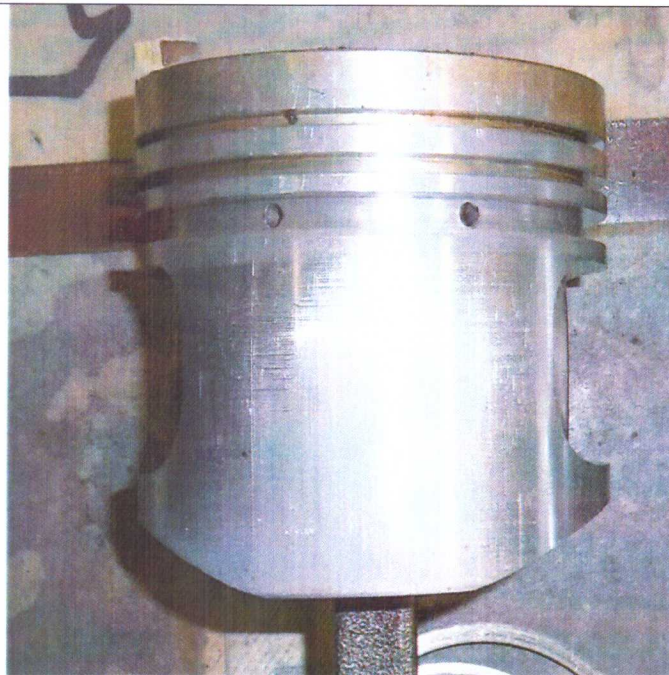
Внешний вид боковой поверхности поршня первого цилиндра по окончании длительных испытаний двигателя при работе на базовом масле Castrol EDGE с добавкой нанокompозита Amortect PROOF
